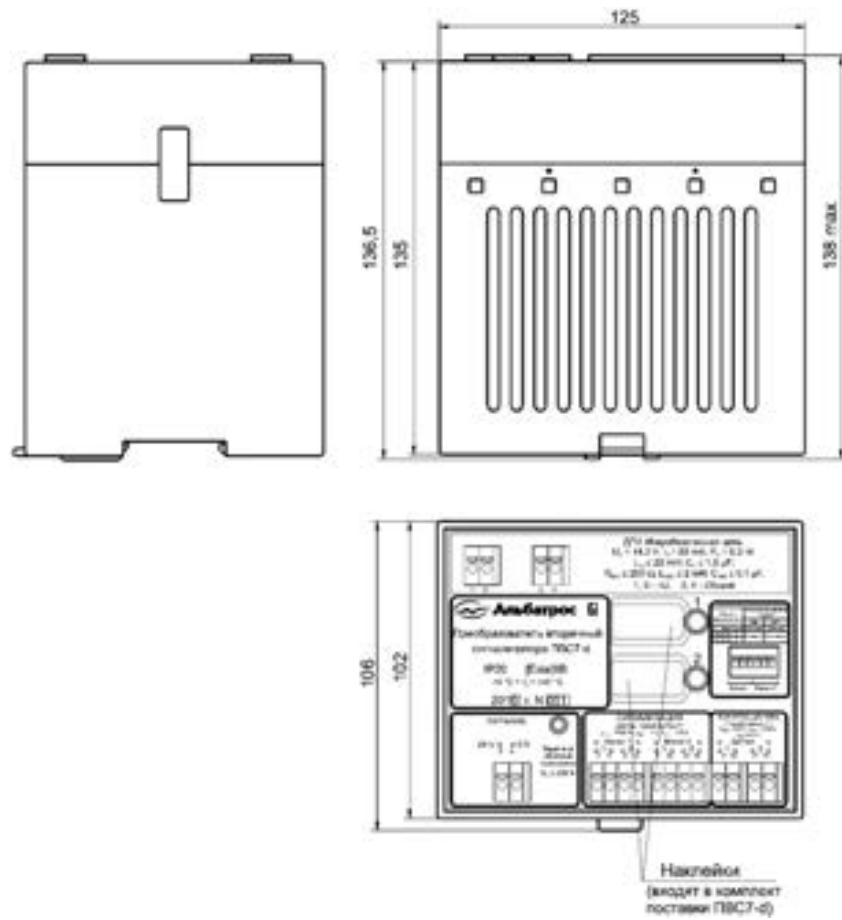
Габаритные размеры вторичного преобразователя ПВС7-d
